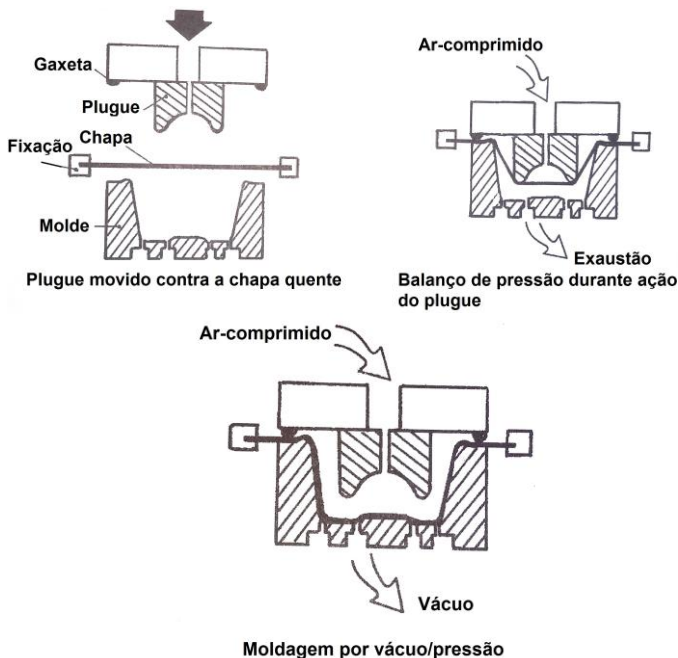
Pré-moldagem com plugue seguida de moldagem por pressão.
